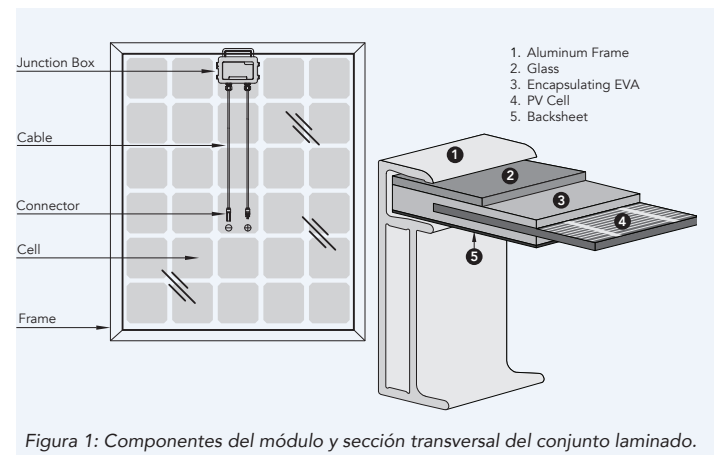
Componentes del módulo y sección transversal del conjunto laminado.
